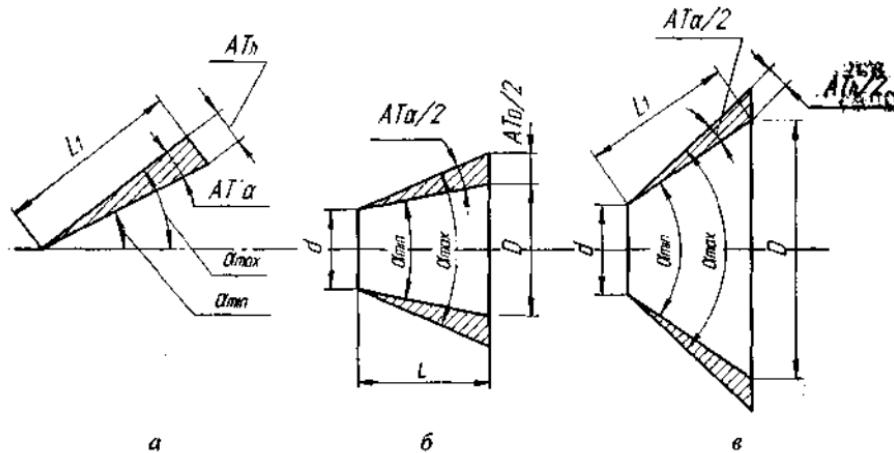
Расположения полей допусков углов и конусов:
